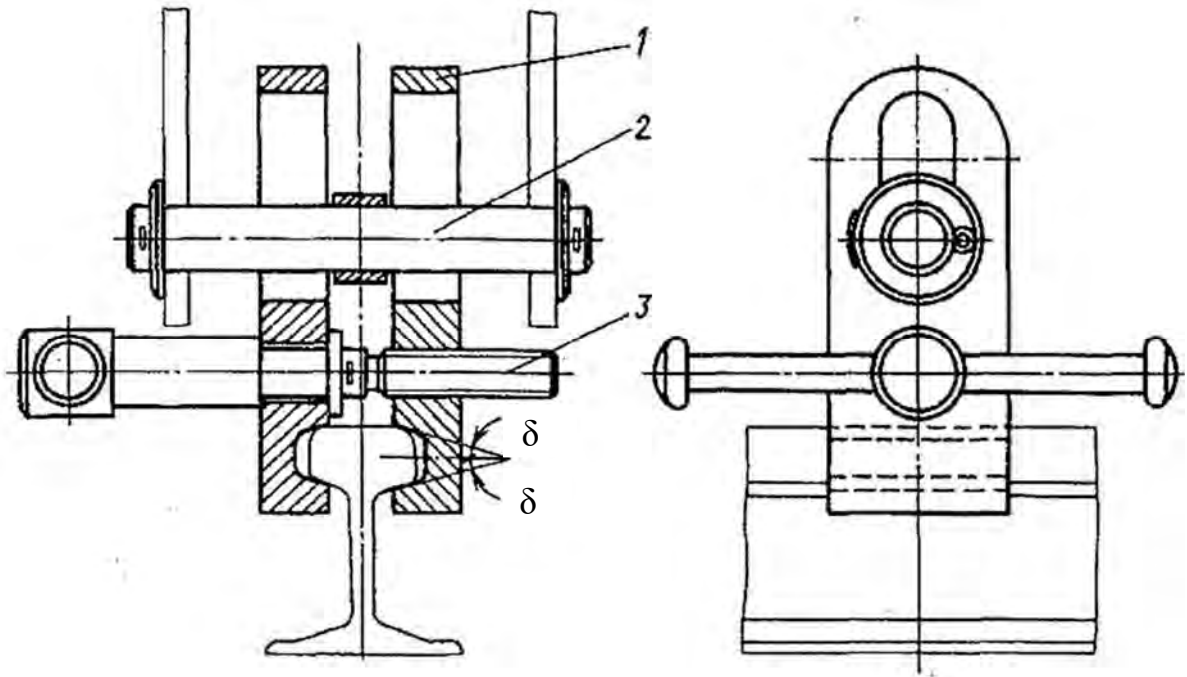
Ручной клещевой захват: 1 – рычаг захвата; 2 – палец; 3 – винт
